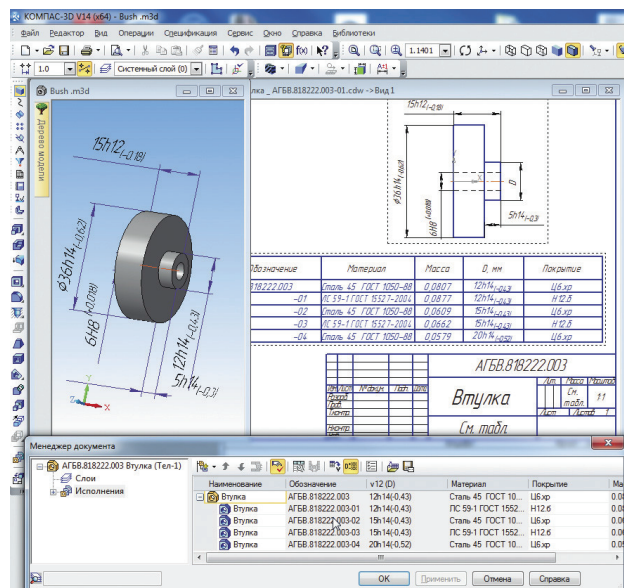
Модель и ассоциативный чертеж детали с исполнениями
